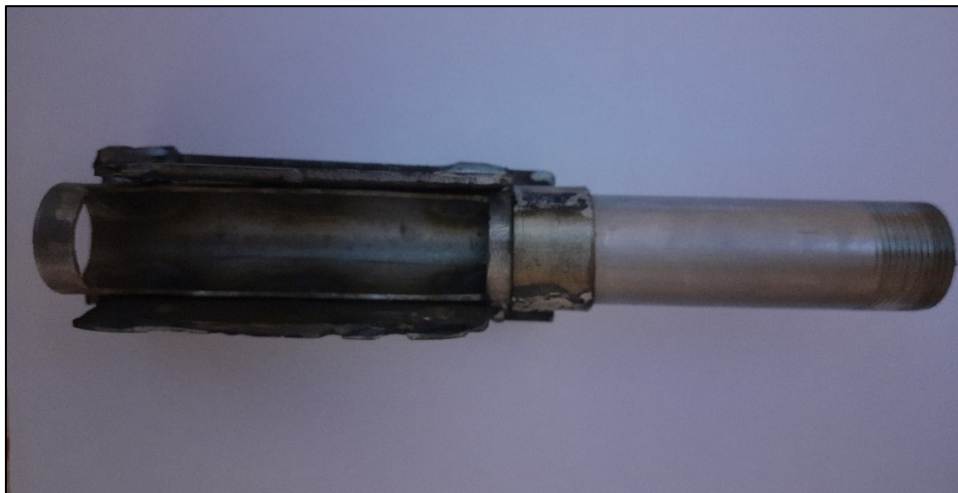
Le tube avec filetage et après la soudure avec des morceaux de fer.
